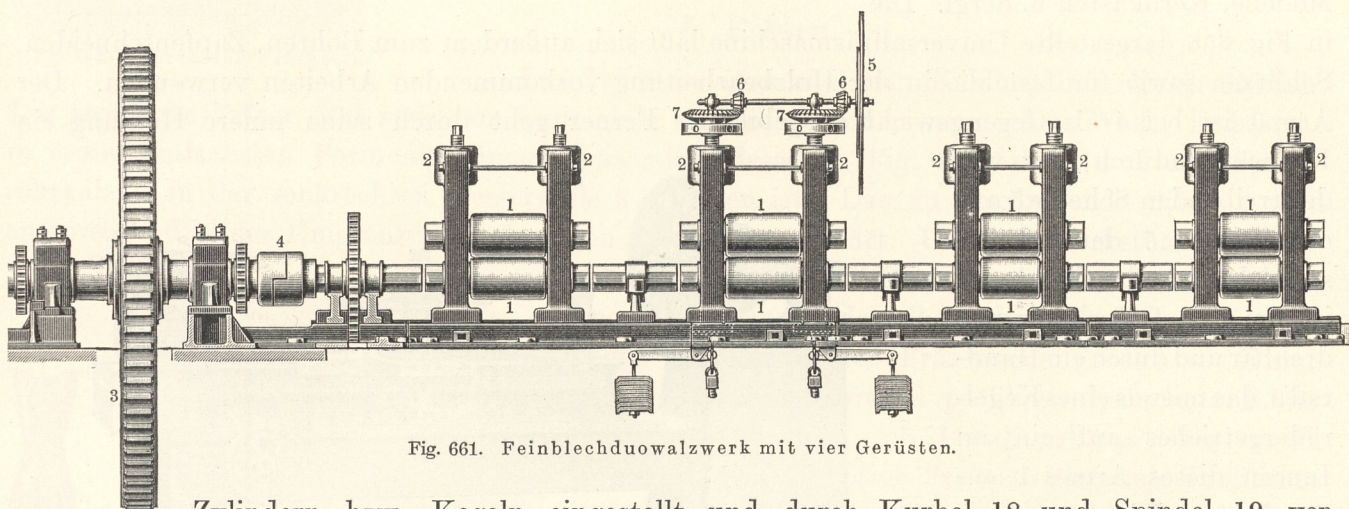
Feinblechduowalzwerk mit vier Gerüsten.
